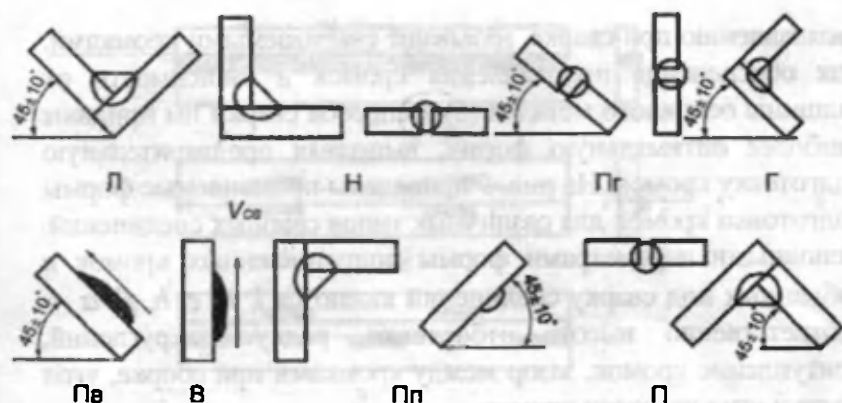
Основные пространственные положения сварки и их обозначения
